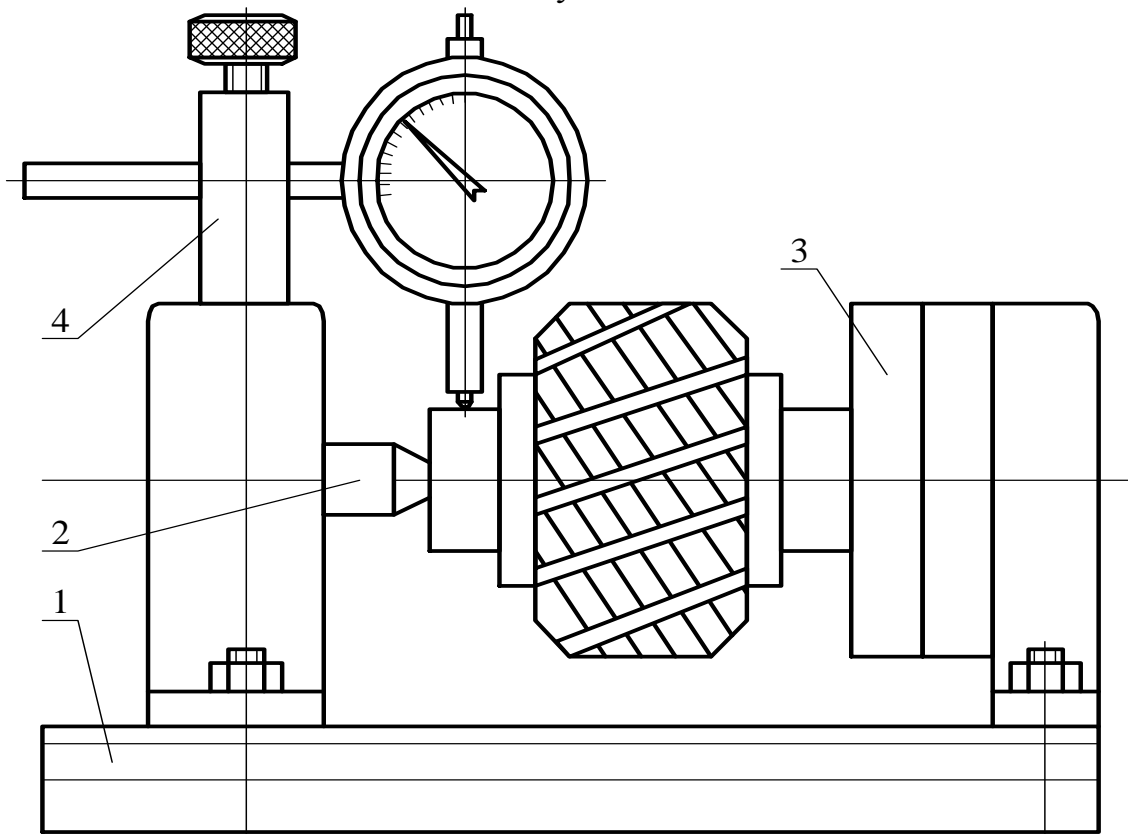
Пристрій для контролю параметрів черв'ячної фрези
